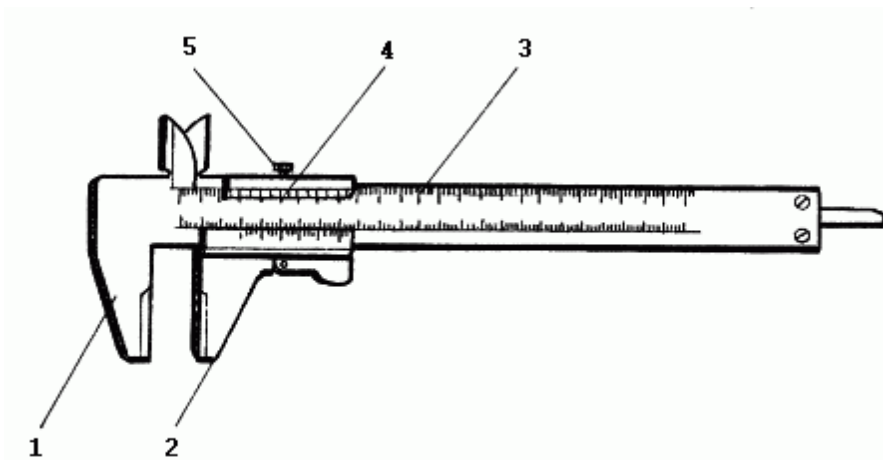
Штангенциркуль: 1 – измерительные губки; 2 – рамка; 3 – штанга; 4 – нониус; 5 – стопорный винт
